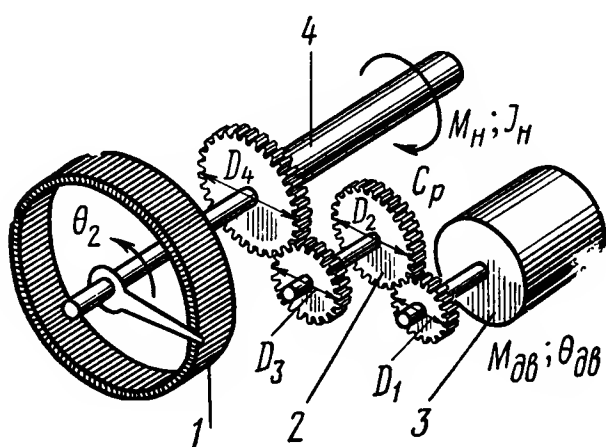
Кинематическая схема редуктора системы автоматического регулирования с цилиндрическими шестернями:
